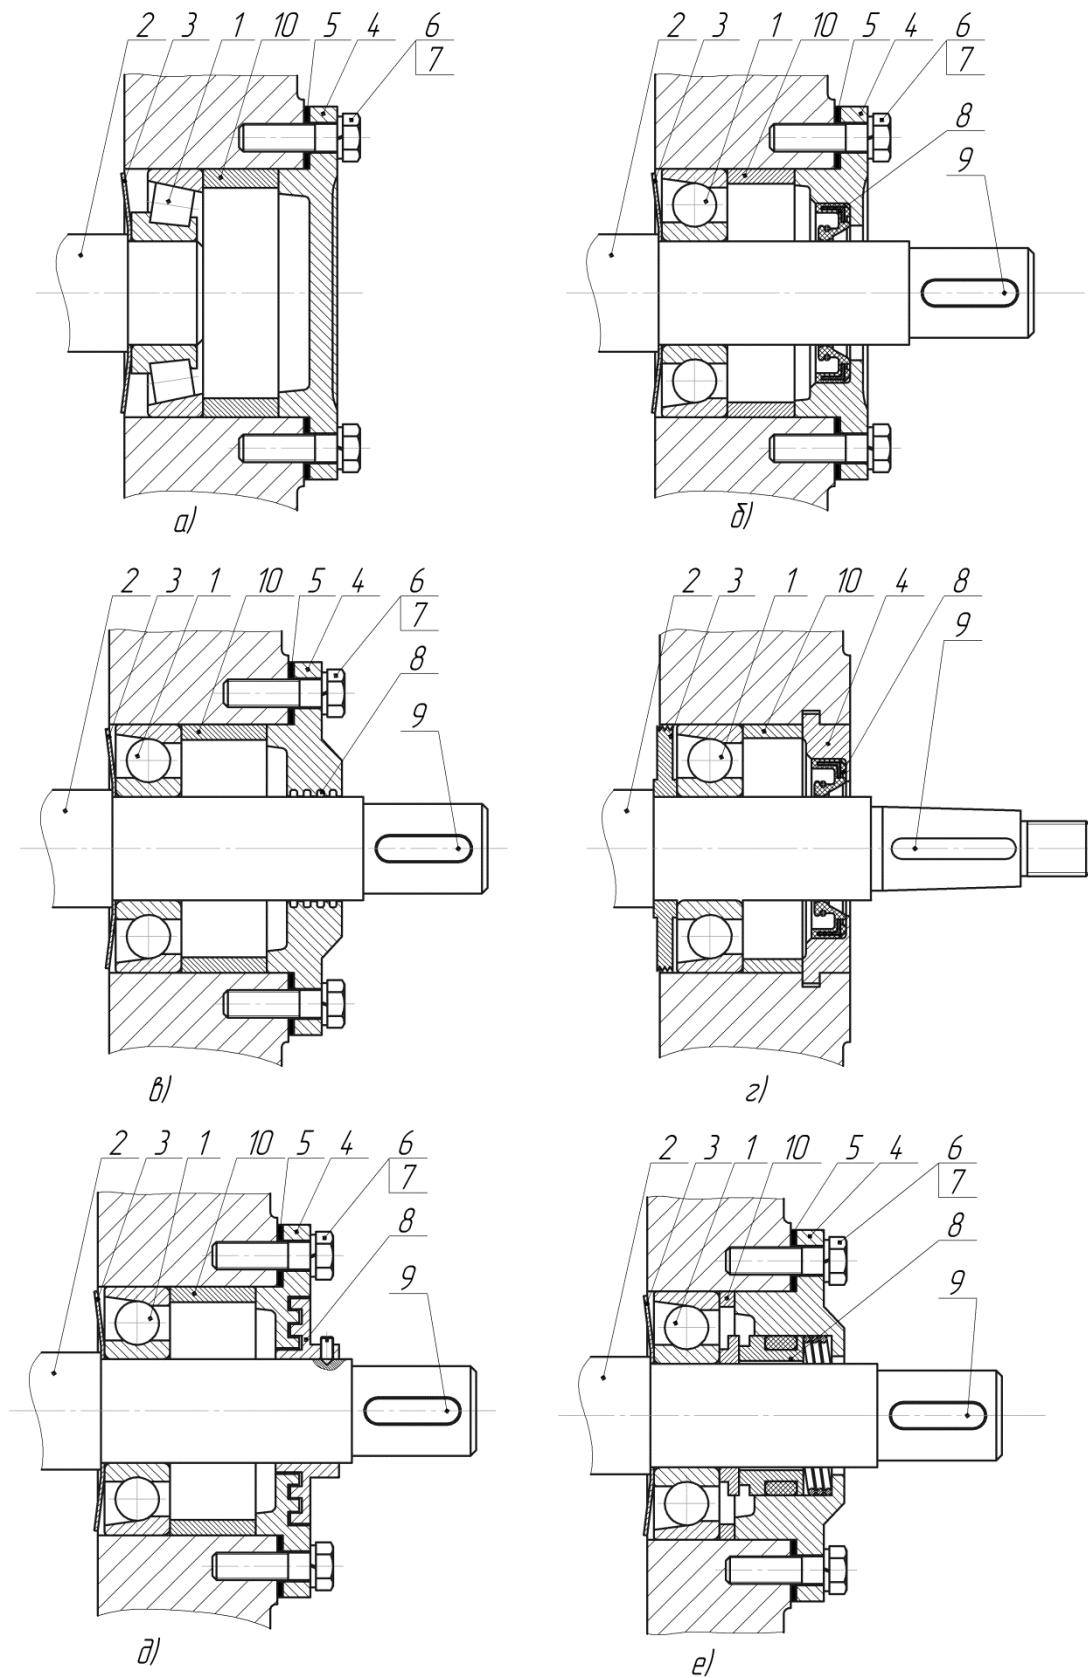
Основные типы подшипниковых узлов и уплотнительных устройств, применяемые в современных редукторах
